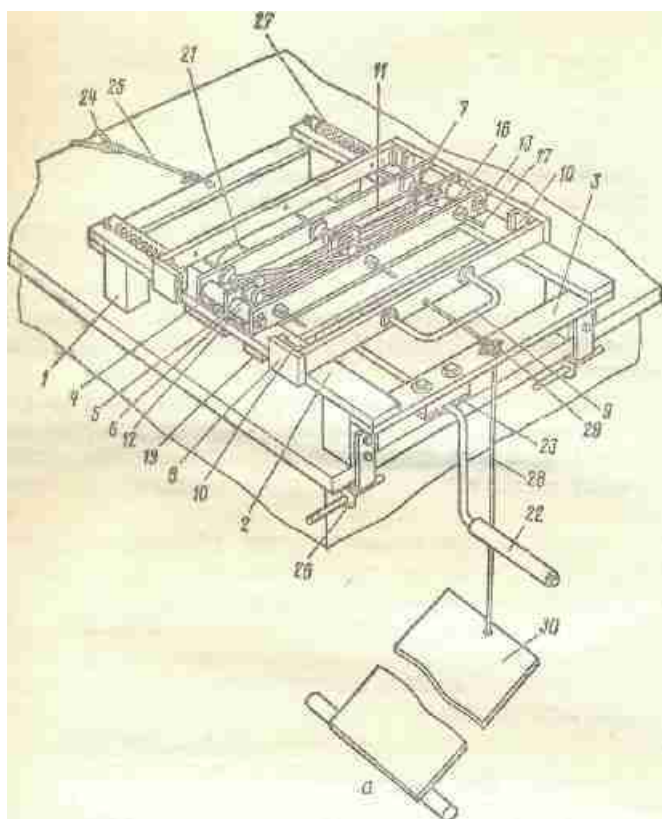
Приспособление с комбинированным приводом для сверления отверстий в планках ульевых рамок
